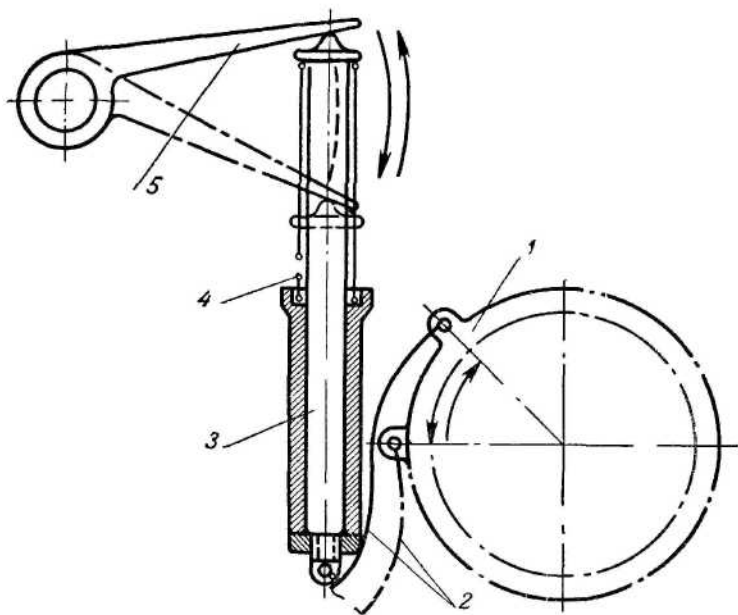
Кинематическая схема привода и взвода затвора объектива И-22: 1 — рычаг затвора объектива; 2 — капроновая жилка - тяга привода; 3 — щиток привода; 4 — возвратная пружинка штока; 5 — рычаг привода взвода затвора
